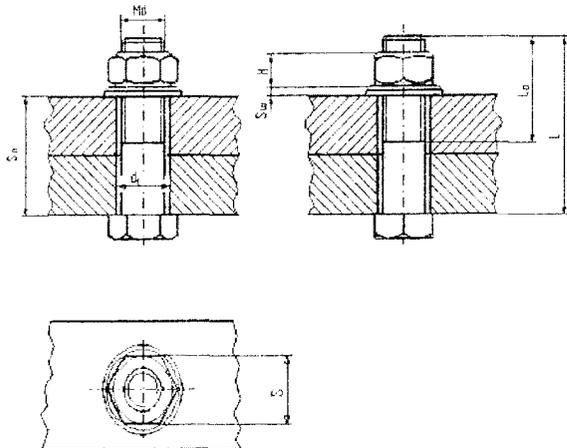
Изображение болтового соединения (на чертеже буквенные обозначения размеров следует заменить цифровыми значениями)
